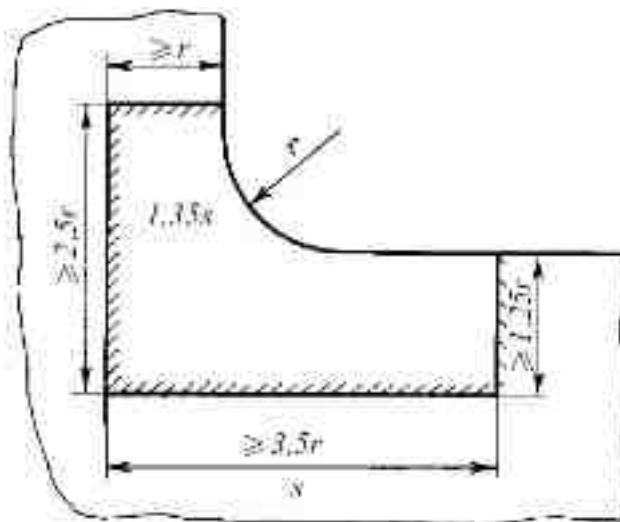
Размеры утолщённого сварного листа
